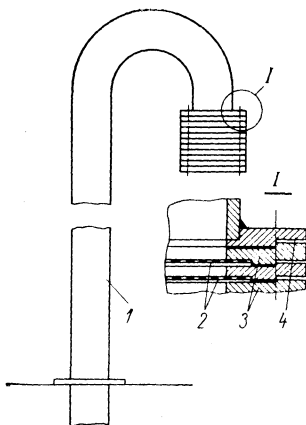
Защитное противовзрывное устройство для воздушных труб замещения и вентиляции:
